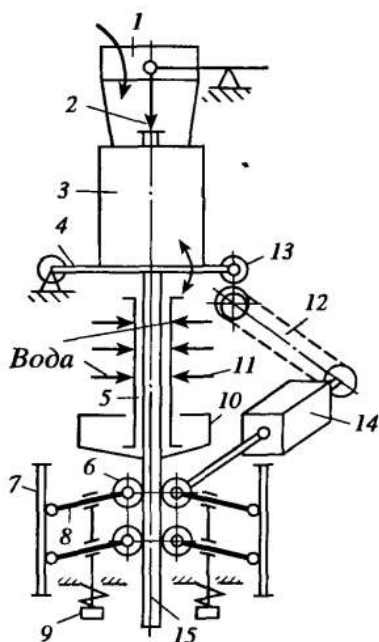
Схема вертикальной двухручьевой МНЛЗ для отливки ватербасов
